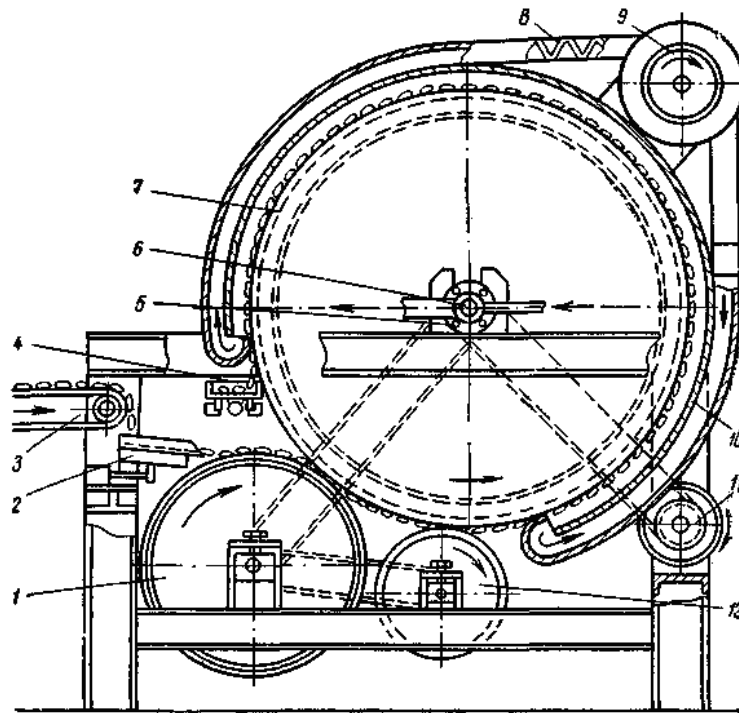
Морозильний апарат барабанного типу для заморожування вологих продуктів неправильної форми: 1 – живильний барабан; 2, 4 – вібрототики; 3 – вхідний конвеєр; 5 – підшипники; 6 – вал; 7 – заморожувальний барабан; 8 – повітроохолоджувач; 9 – вентилятор; 10 – кожух; 11 – електродвигун; 12 – прижимний барабан
